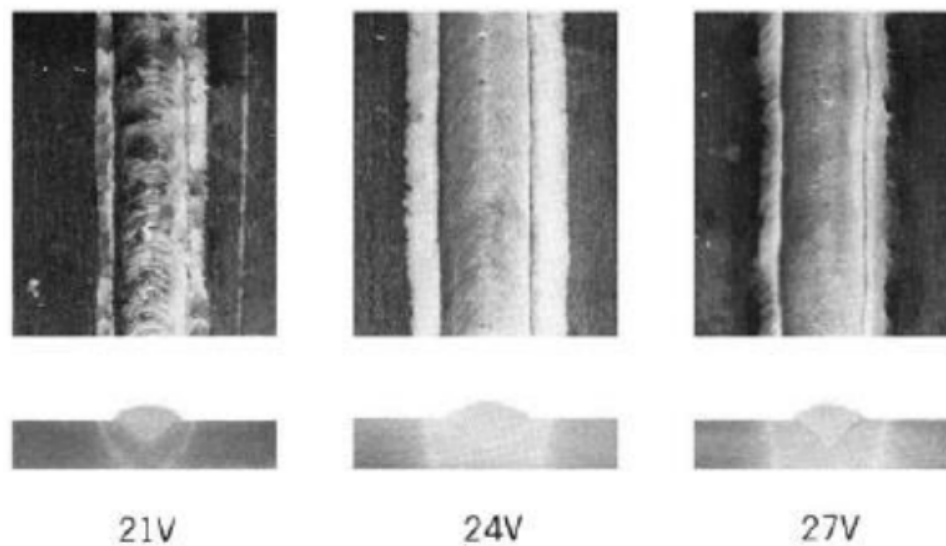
Efeito da tensão de soldadura na penetração da solda [13].
